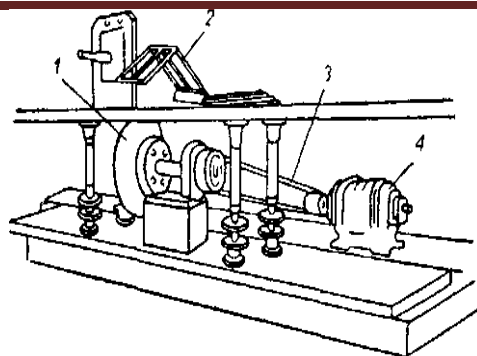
Механическая пила для резки стеклянных трубок: 1—стальной диск с режущей кромкой; 2—защитная рамка; 3—ременная передача; 4—электродвигатель.
